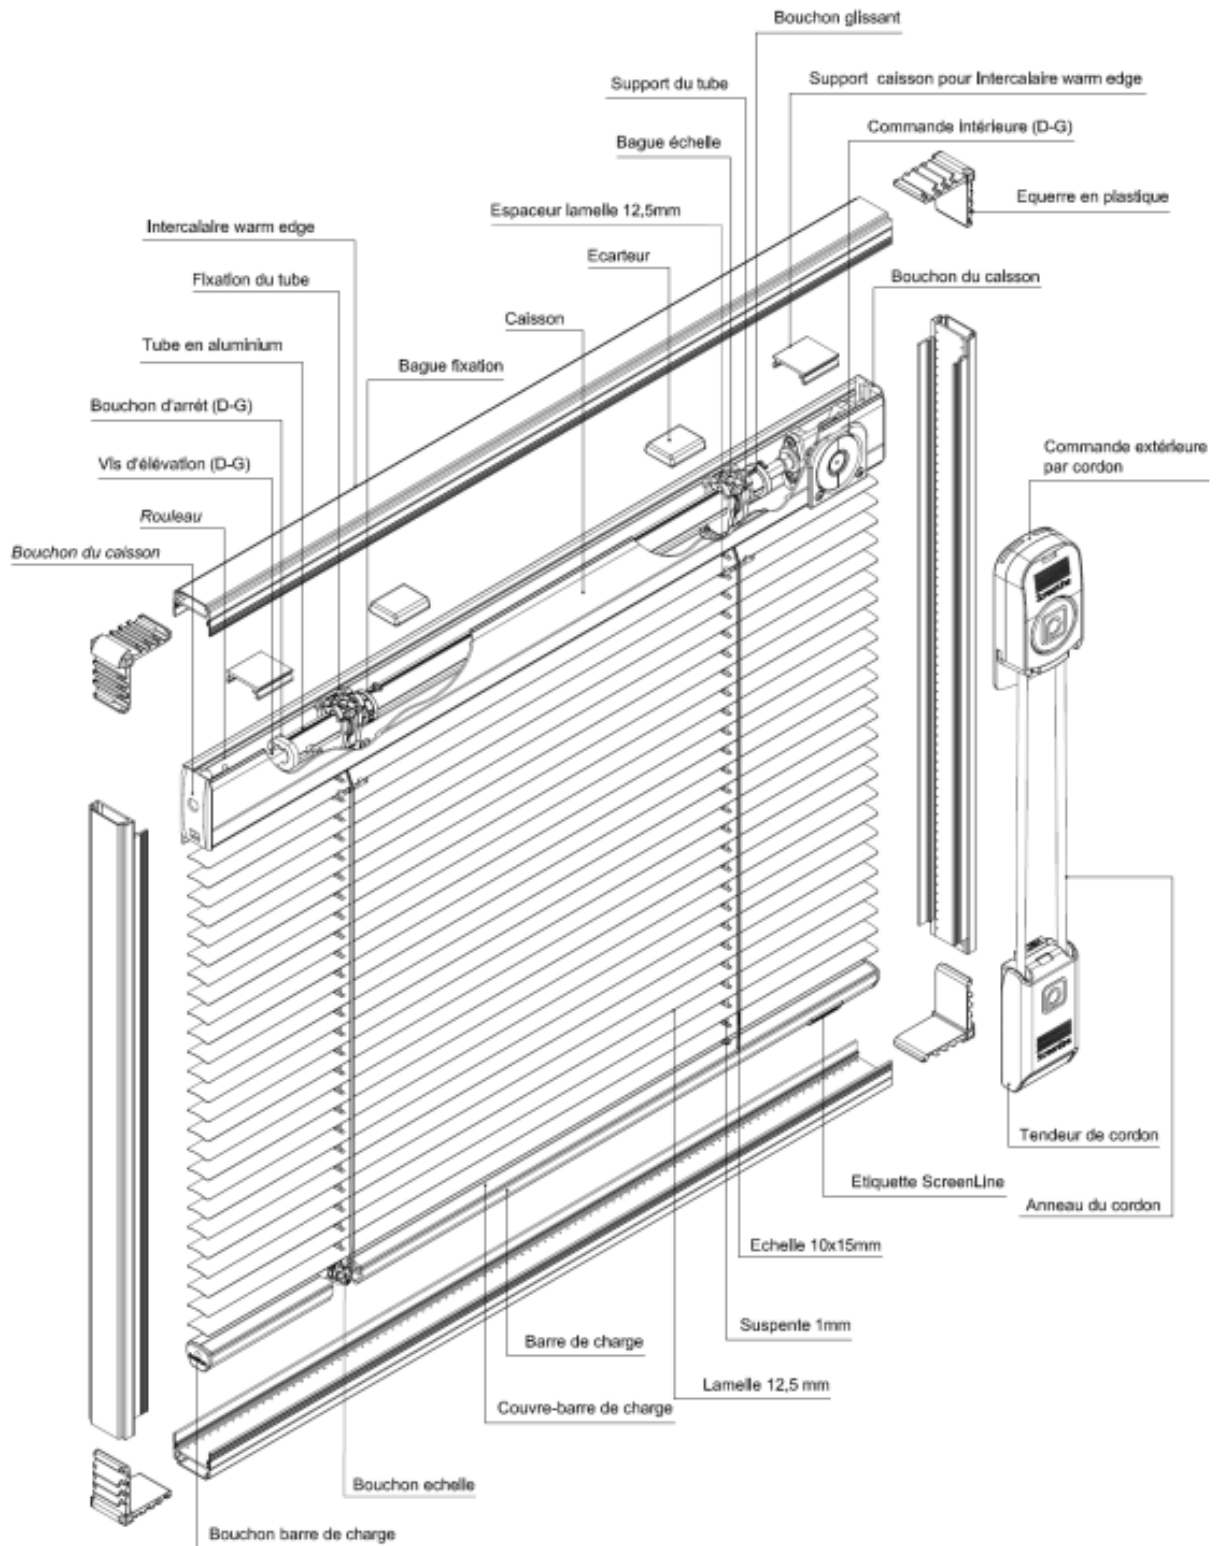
Vue d'ensemble éclatée avec espaceur Warm Edge SL 20 ou SL 22
